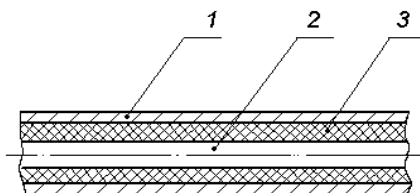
Коаксиальный электрод-нагреватель в разрезе
